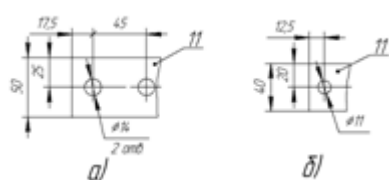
Контактный вывод разъединителя со стороны подвижной колонки
